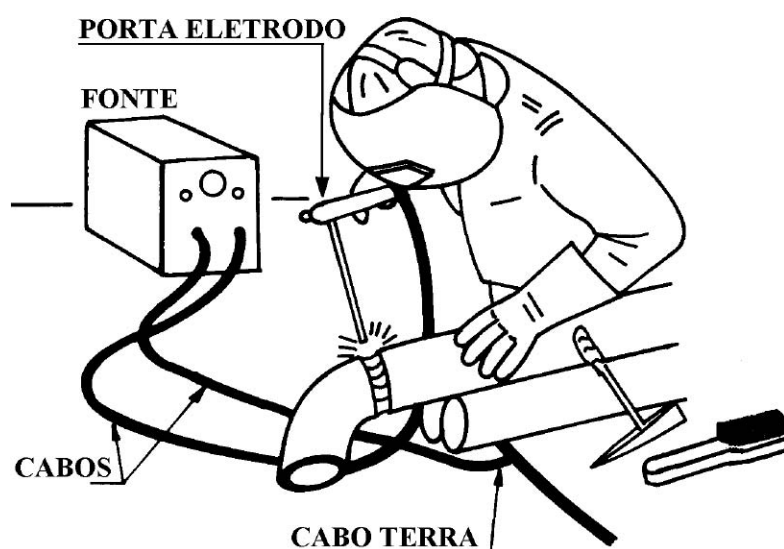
Equipamento para soldagem SMAW (Modenesi e Marques, 2006).
